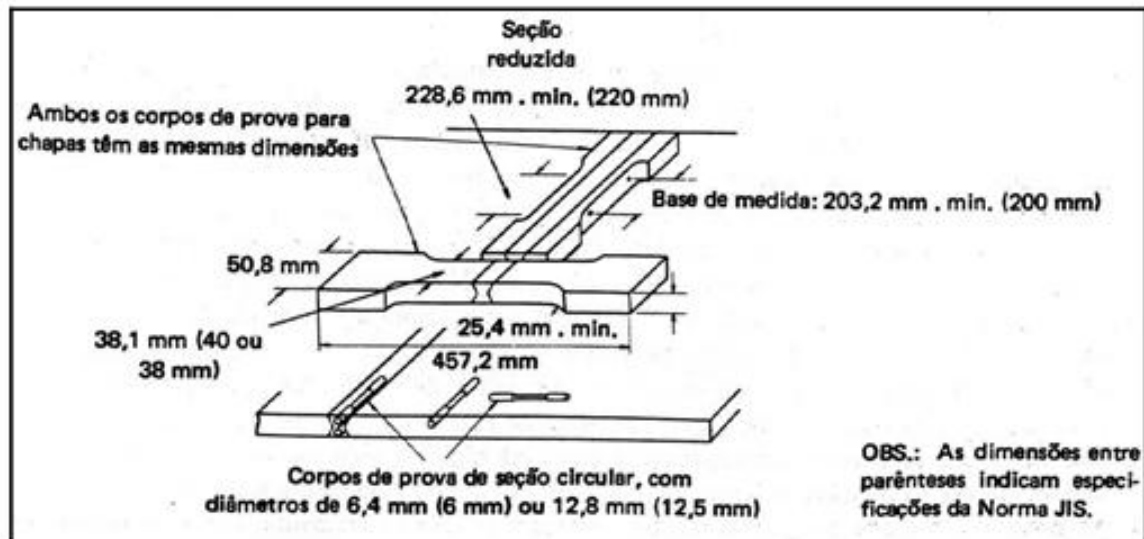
Corpos de prova típicos para ensaios de tração utilizados em soldagem (segundo a AWS).
